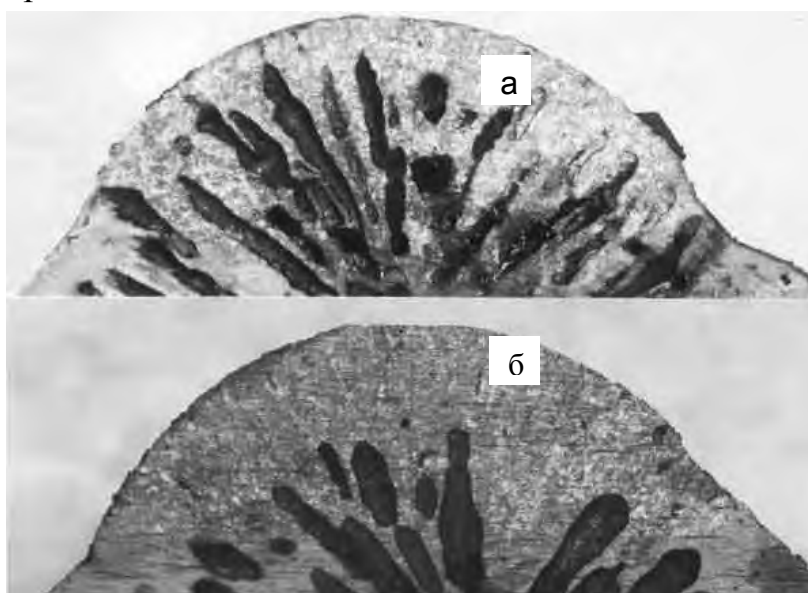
Поверхностная корка плотного металла недостаточной (а) и нормальной (б) толщины в угловых пробах из слитков кипящей стали
